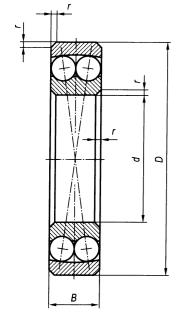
Подшипник шариковый радиальный сферический двухрядный с закрепительной втулкой серий 11200, 11300, 11500 и 11600
